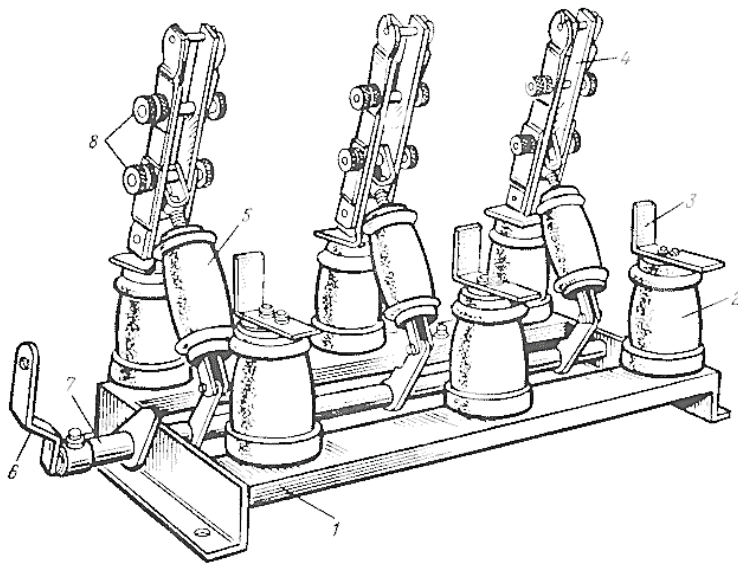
Трехполюсный разъединитель вертикально-поворотного типа.
